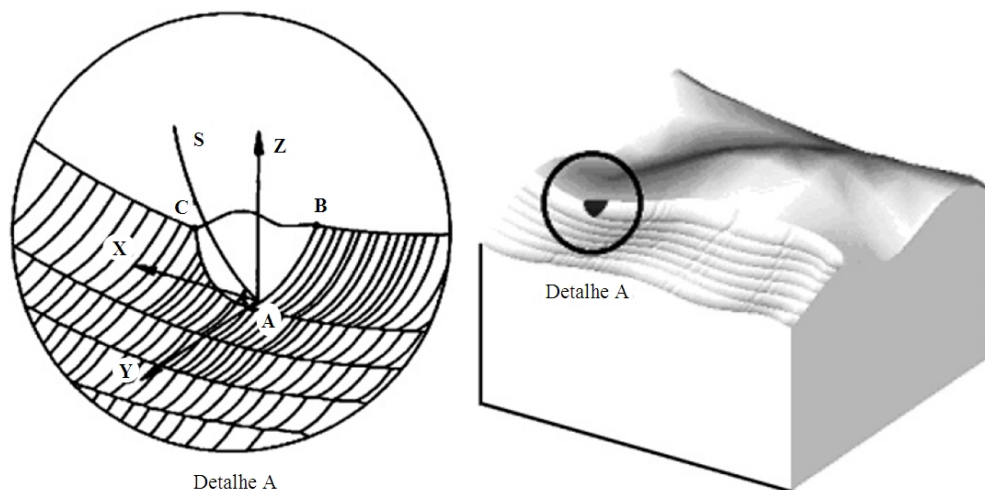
Superfície usinada com fresa de topo esférico e detalhe da seção de corte [14]
